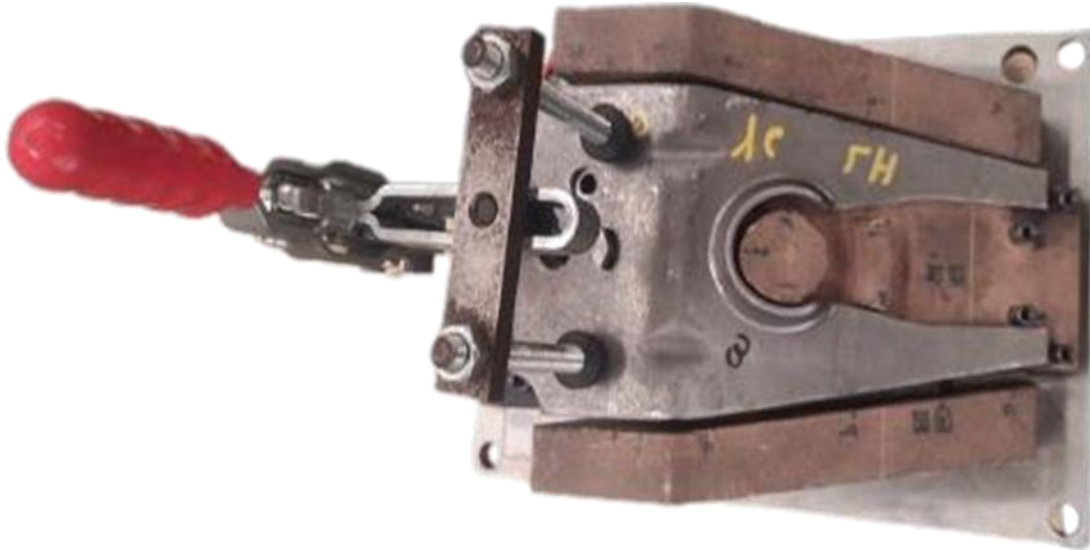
Jig de calidad para parte estampada. Fuente: YMEX 2024
